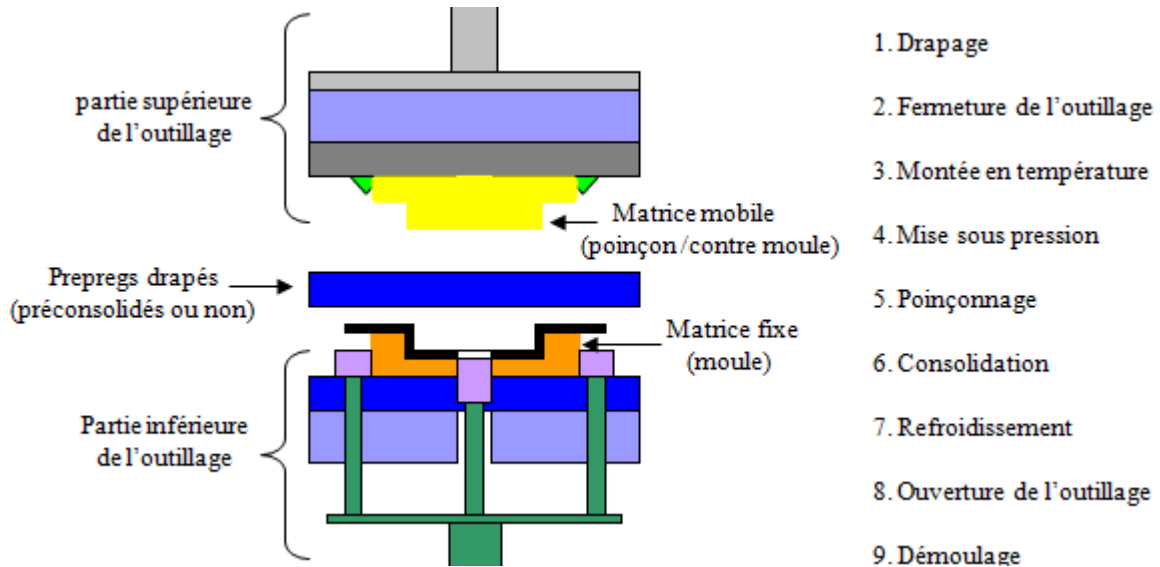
Principe du procédé Carbone Forgé de moulage par compression à chaud et par voie sèche
